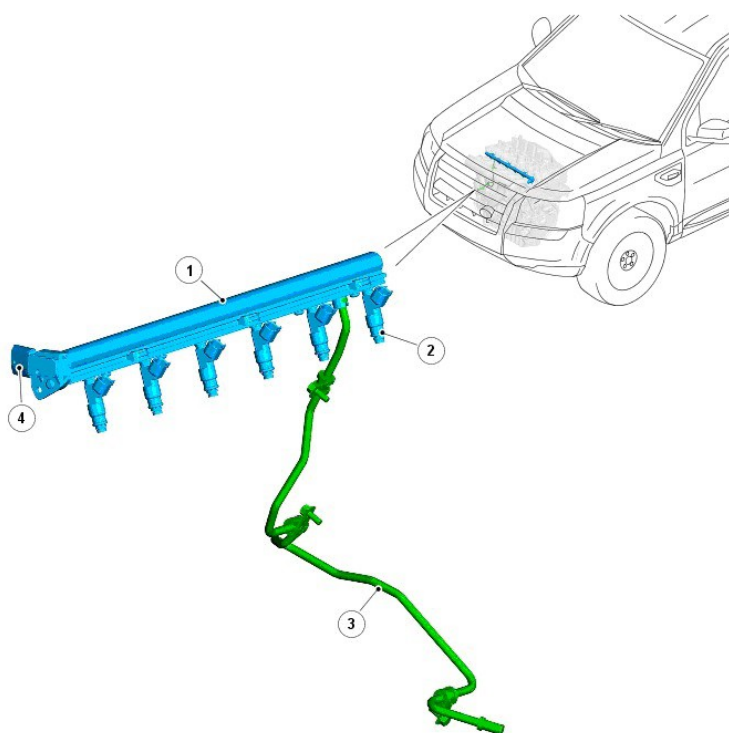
Расположение элементов системы подачи топлива и органов управления бензинового двигателя 3.2L I6 Freelander 2
